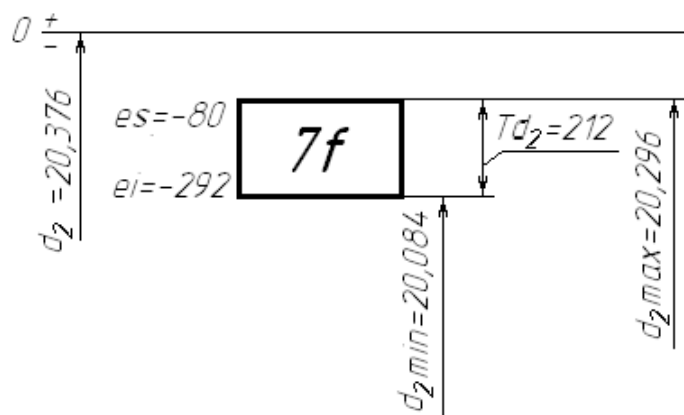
Схема поля допуска на средний диаметр метрической резьбы
